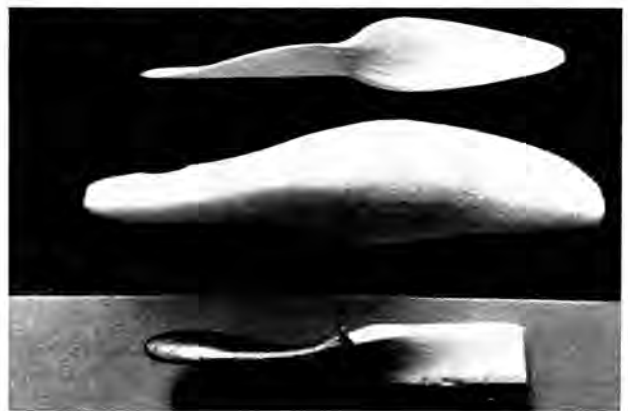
Luftschrauben bzw. Luftschraubenblätter aus gepresstem Isolafros.
